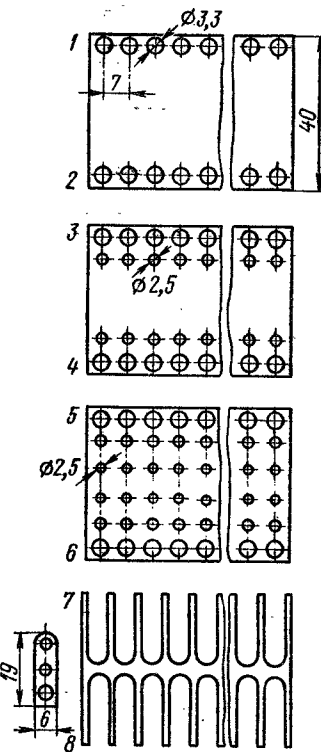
Схема полуавтоматической штамповки по элементам (1—8 последовательность штамповки)
